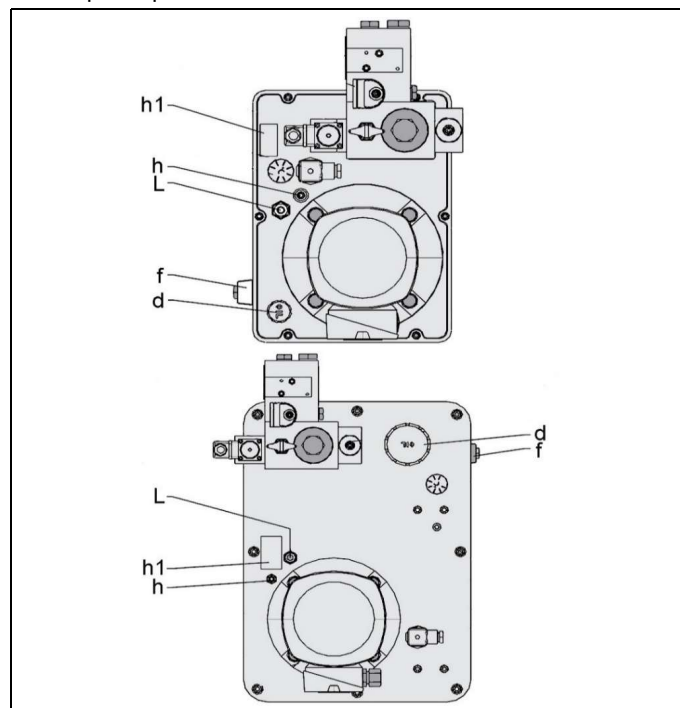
Figure sur le couvercle du groupe hydraulique V11/27/40/63
